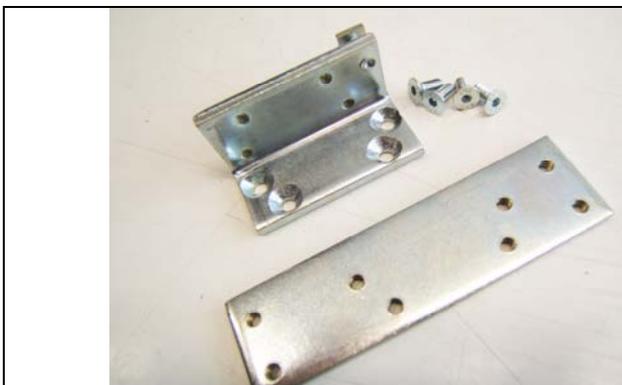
Staffa rettangolare lunga e staffa ad L, lato anta – Long rectangular plate and L plate, wing side
